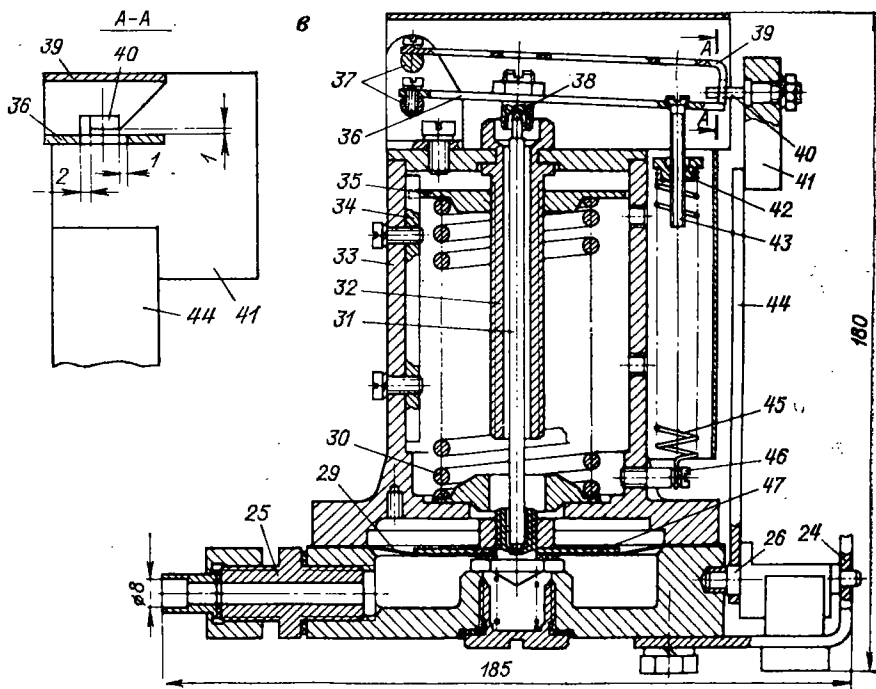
Предохранительный запорный клапан КПН (КПВ).
